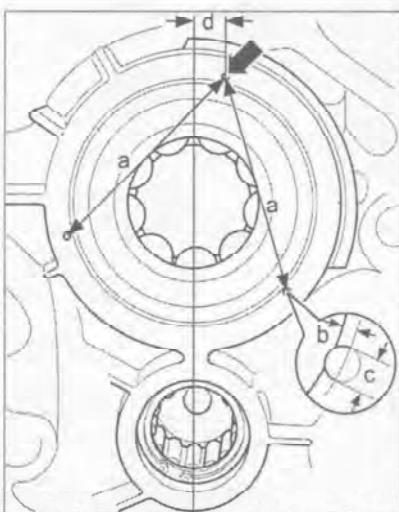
Установка защитной пластины при замене крышки коробки передач.
